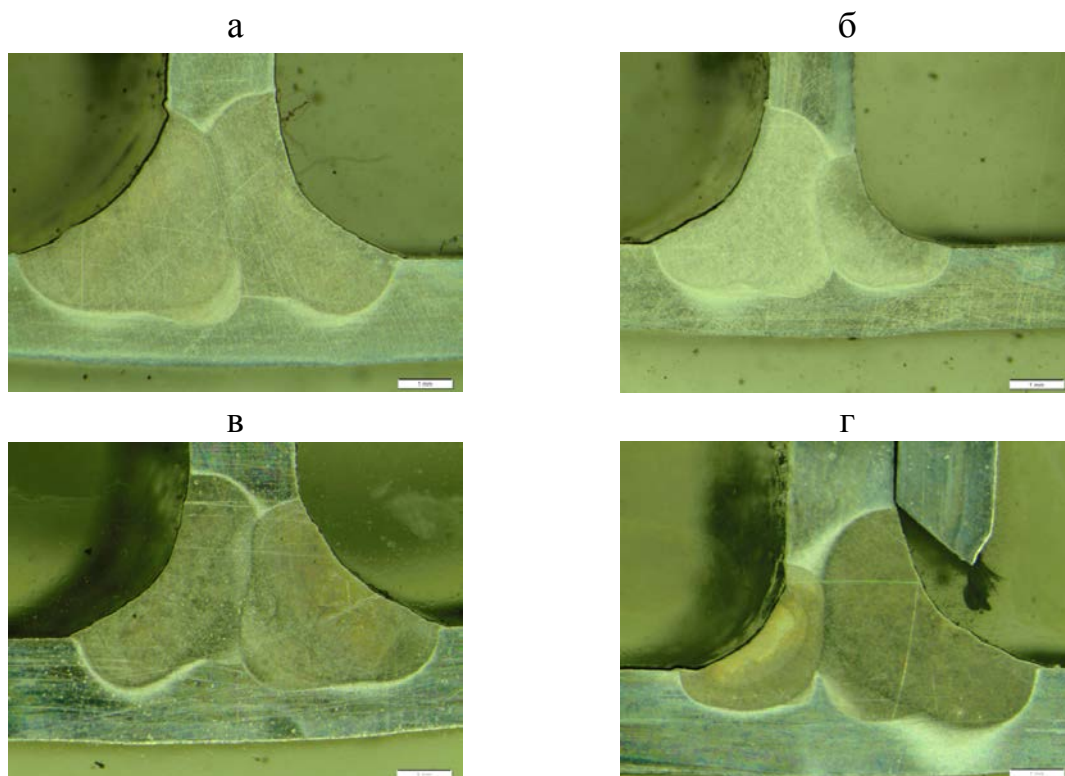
Макроструктура сварных тавровых соединений, выполненных лазерной сваркой по режиму I (а, б), режиму II (в, г) и лазерной сваркой с подваркой (б, г)
